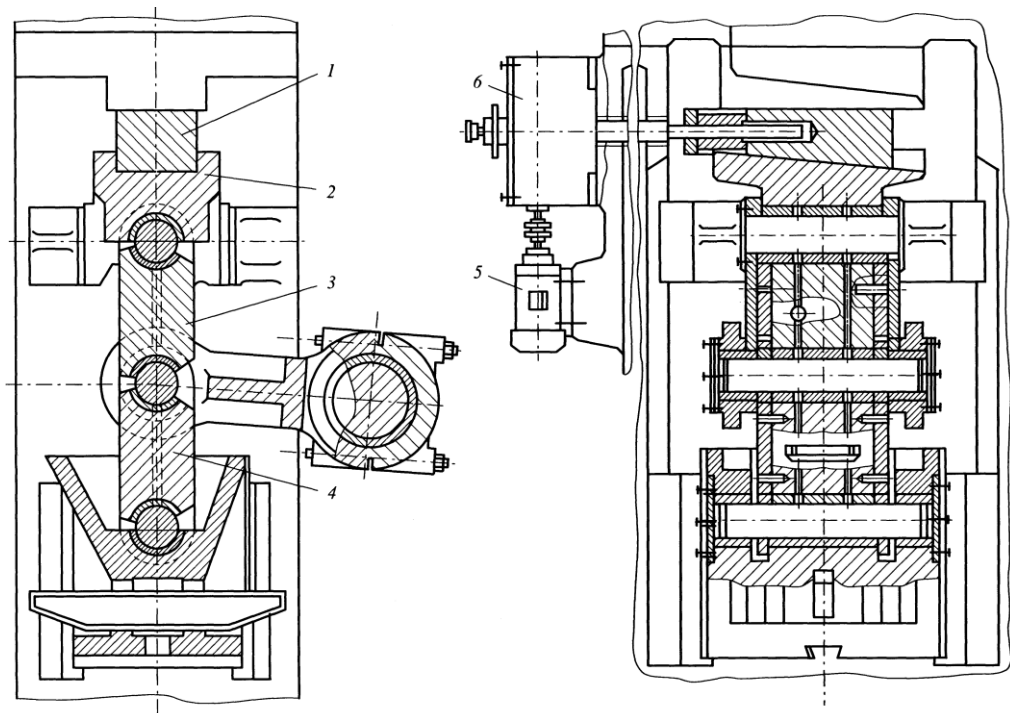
Конструктивна схема кривошипно-колінного механізму: 1 – клин; 2 – опора, 3 – верхня призма, 4 – підвіска повзуна, 5 – електродвигун, 6 – черв'ячний редуктор
